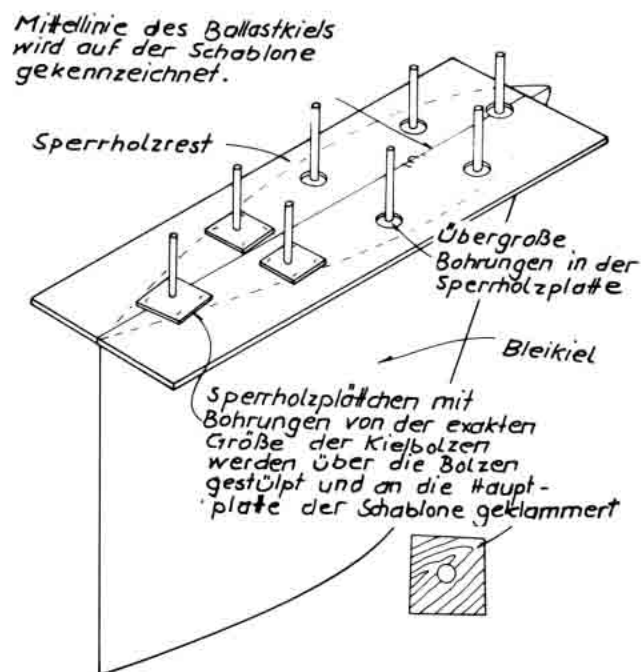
Herstellen einer Kielbolzen-Schablone.
